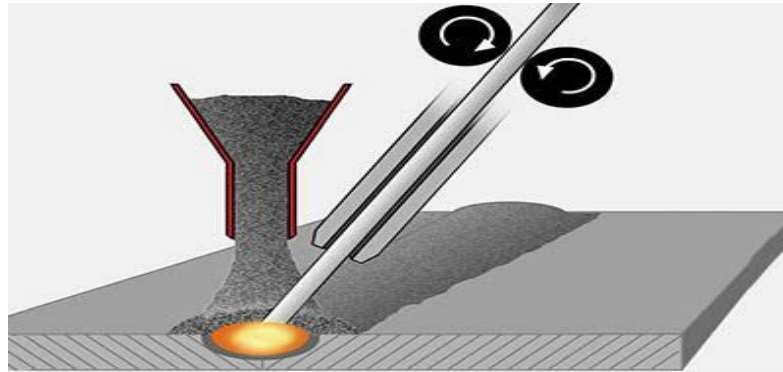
Soudage à l'arc sous flux [10]
